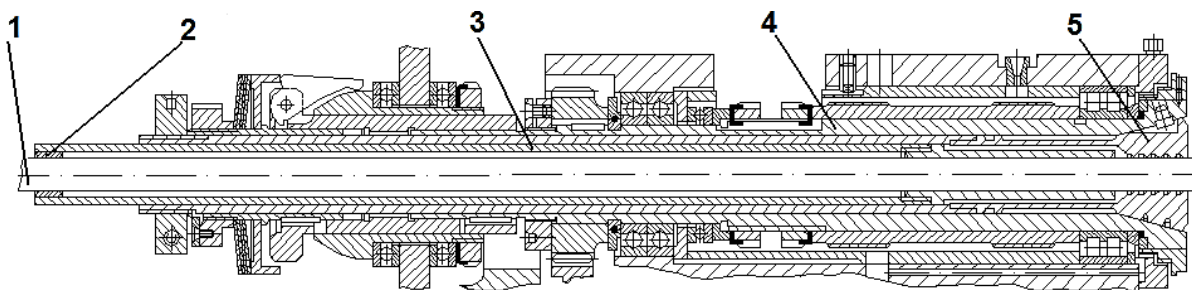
Шпиндельний вузол токарного автомата 1Б240:
